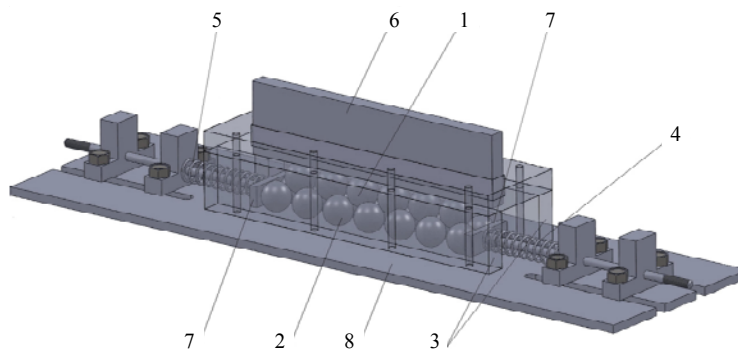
Схема шарикового передаточного механизма: 1 — верхние шарики, 2 — нижние шарики, 3 — боковые направляющие, 4 и 5 — пружины, 6 — ползун, 7 — упоры, 8 — корпус
